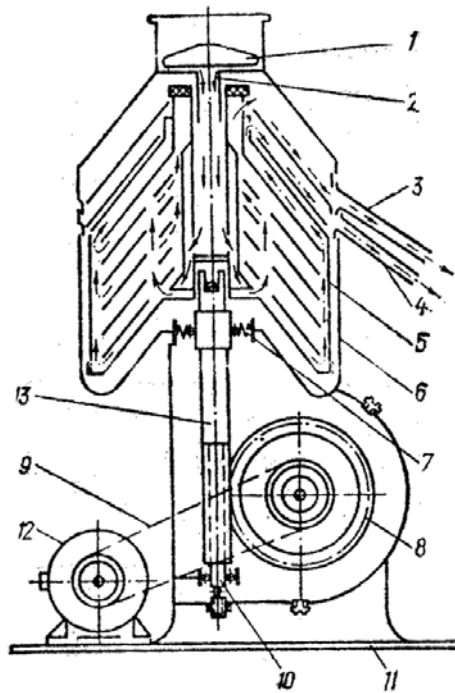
Структурно-кінематична схема сепаратора СОМ-3-1000: 1 – поплавок; 2 – центральна трубка; 3 – збірник вершків; 4 – збірник відвійок; 5 – барабан; 6 – корпус; 7 – верхня опора веретена; 8 – шестерня; 9 – клинопосова передача; 10 – нижня опора; 11 – станина; 12 – електродвигун; 13 – веретено
